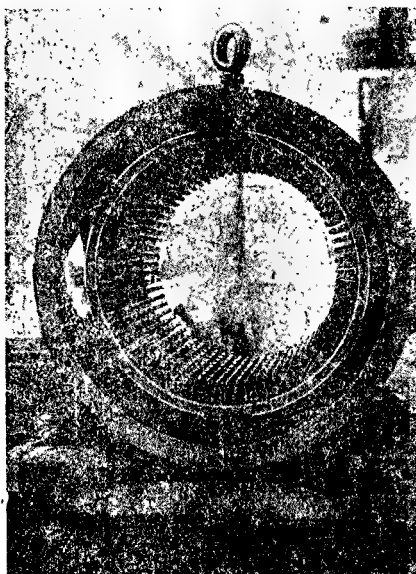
Собранный и распиленный статор двигателя типа PRV 243 п—1500 200 kW, 6000 V.
